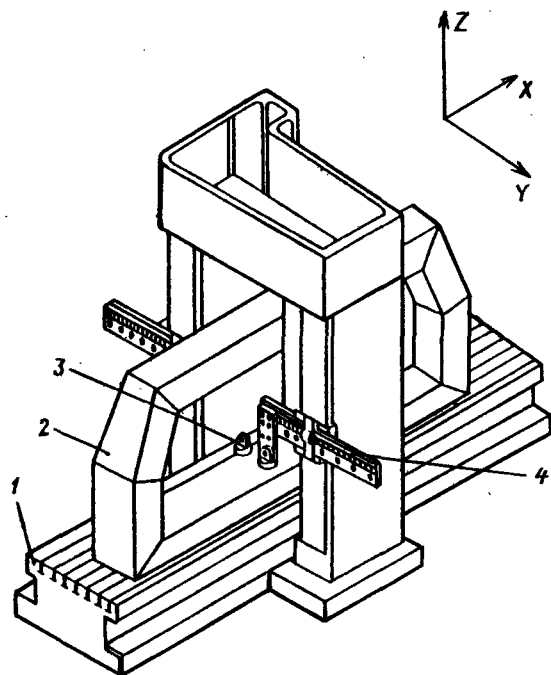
Монтаж стапеля на стенде МС-636Ф-2-11:
